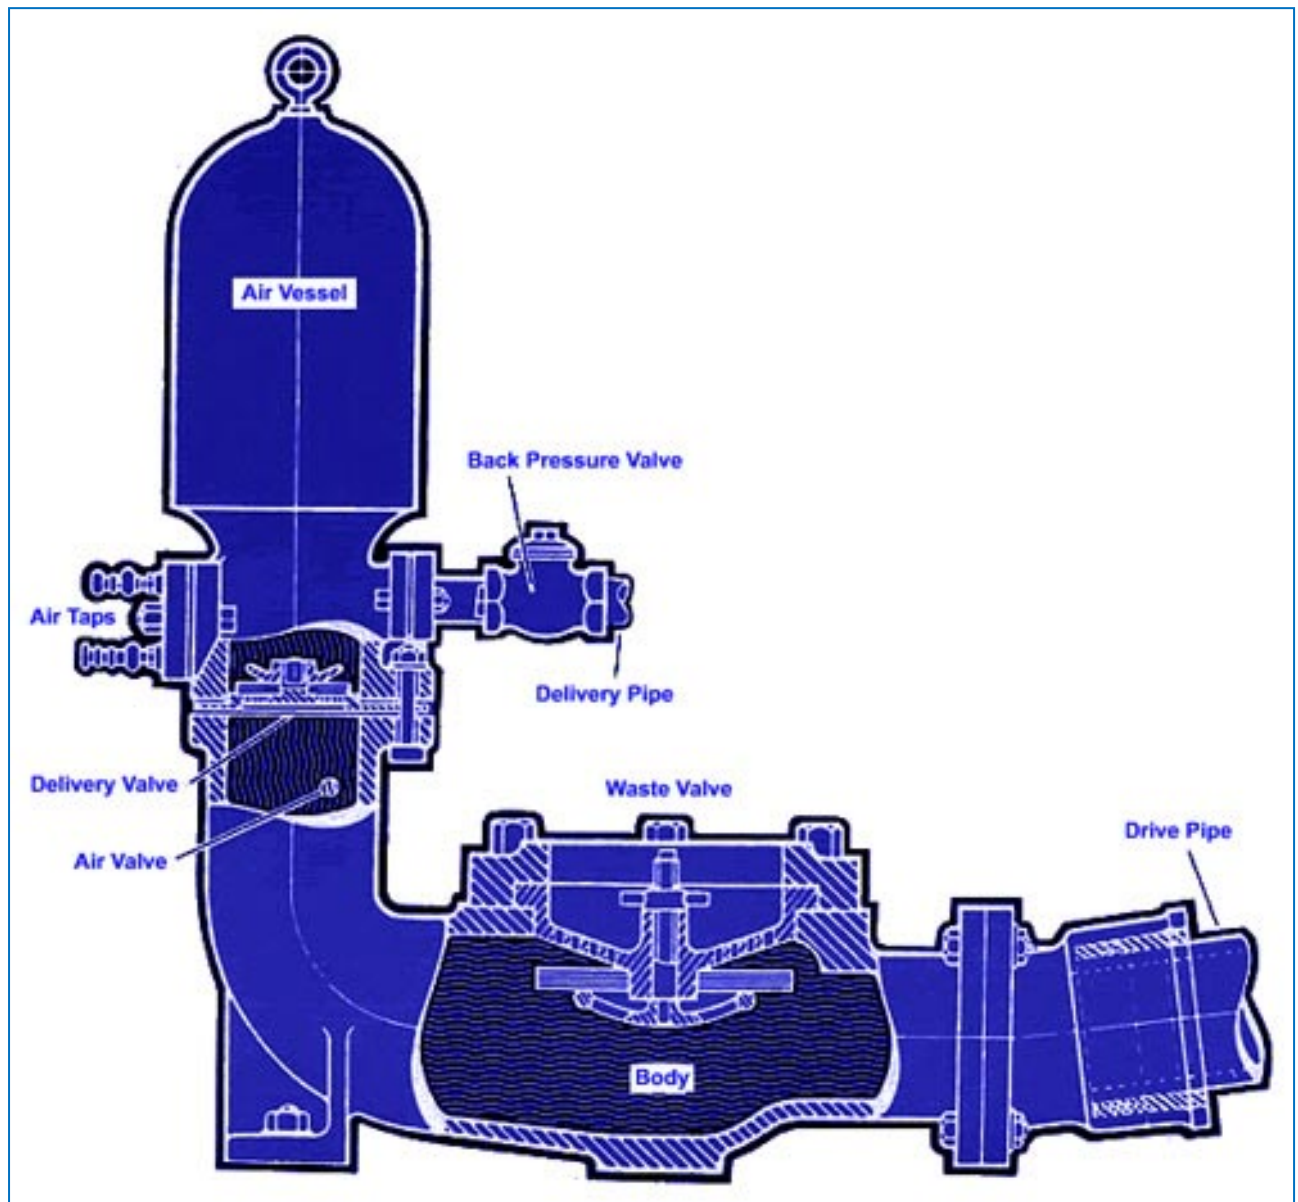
Las diferentes partes de la bomba de ariete Hydram Blake.
